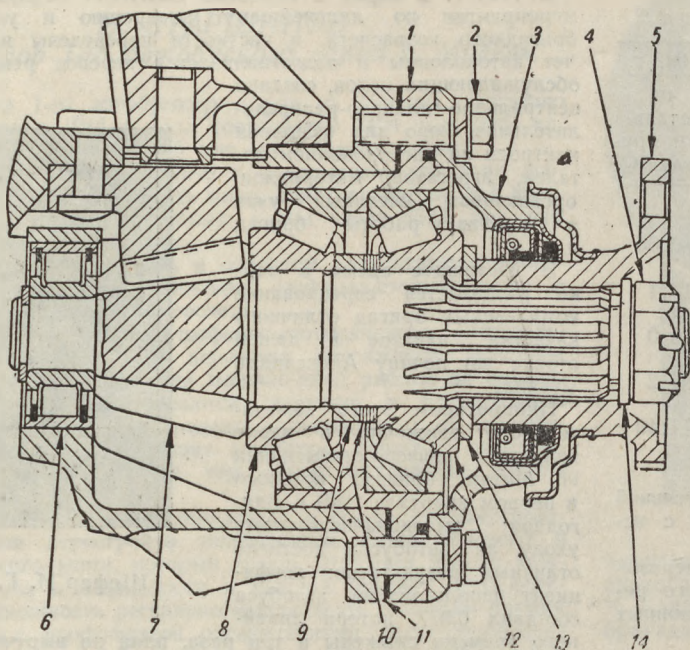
Ведущая шестерня заднего моста в сборе с муфтой подшипников:
